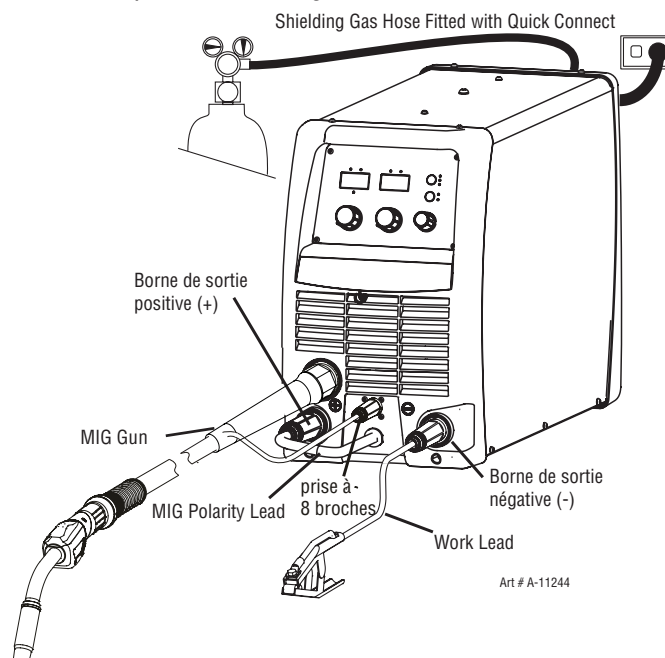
Configuration pour soudage MIG avec fil MIG sous protection gazeuse
